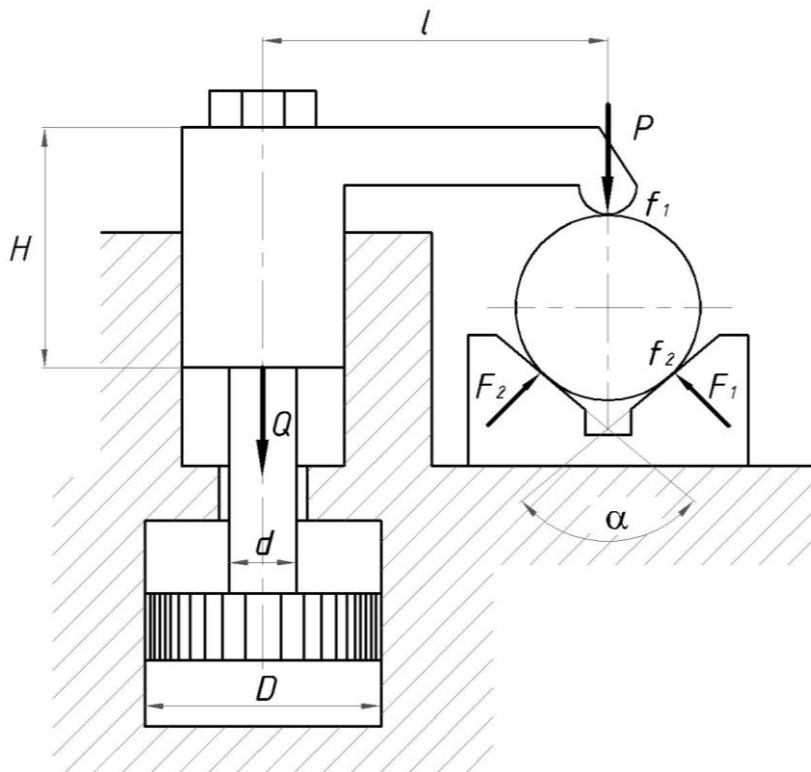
Схема базування та затиску деталі в пристрої для фрезерування рейки
